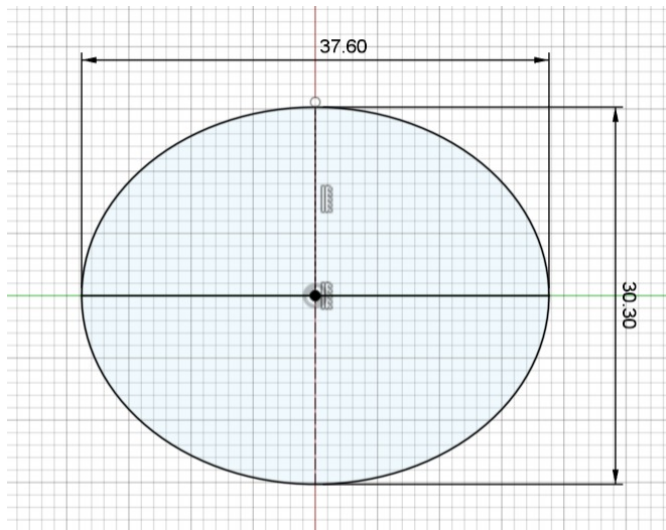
Sección del cuesco para modelado 3D, Elaboración Propia
